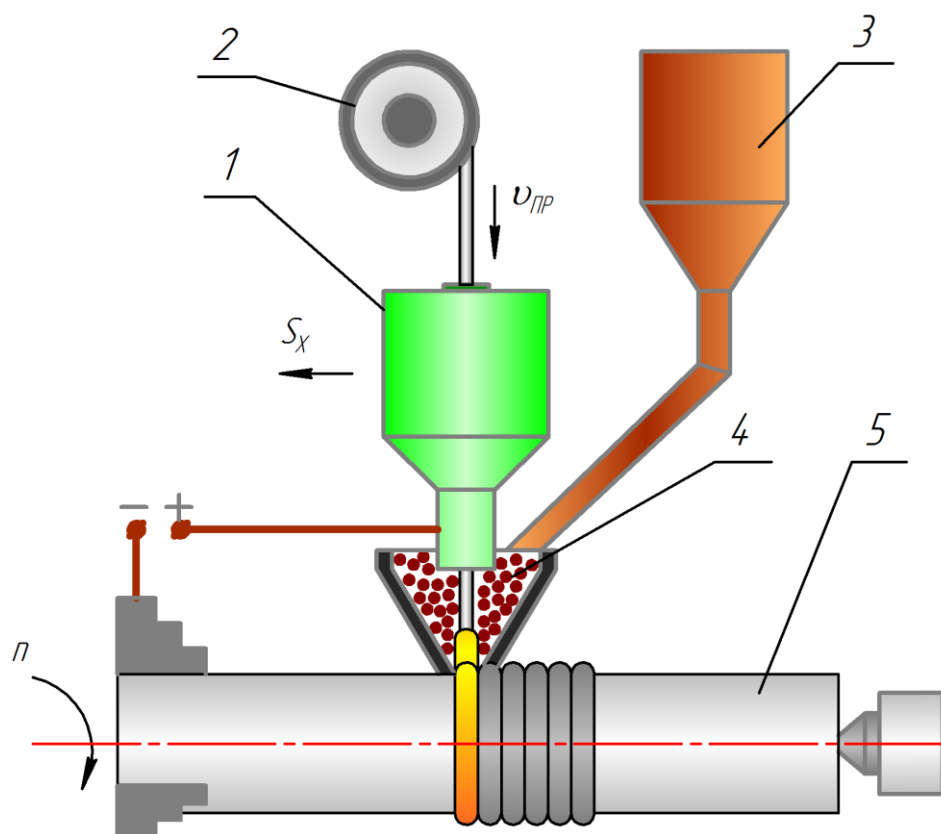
Схема автоматической дуговой наплавки цилиндрических деталей под флюсом:
